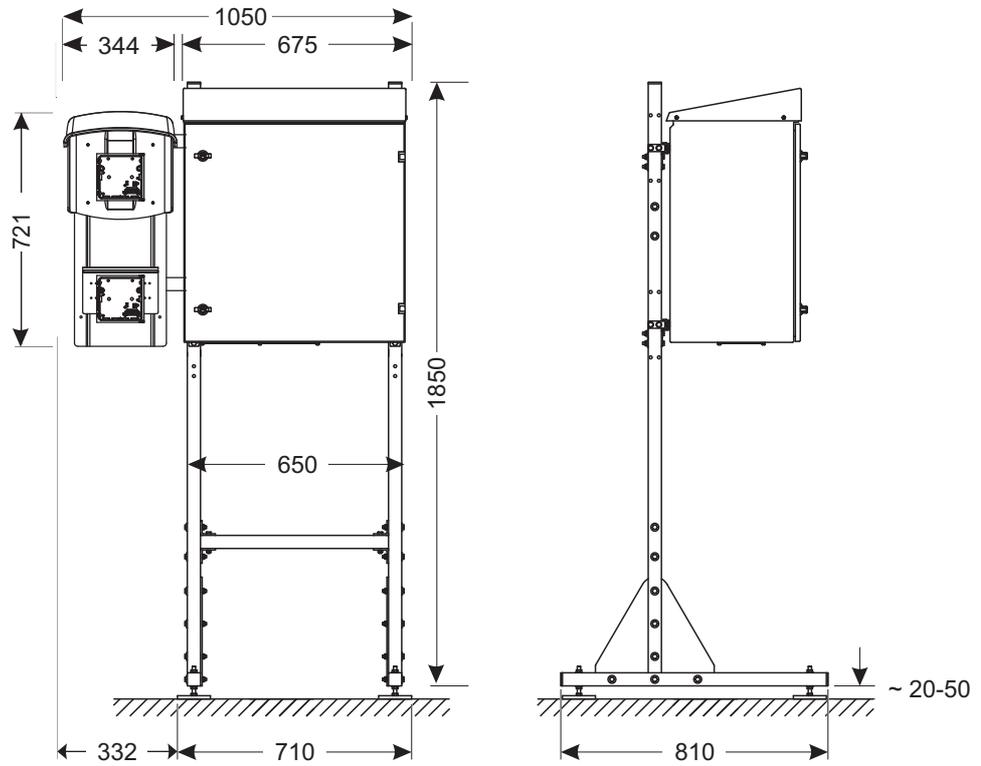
Maßzeichnung Alyza IQ Montage an einer Standsäule (Maße in mm)
